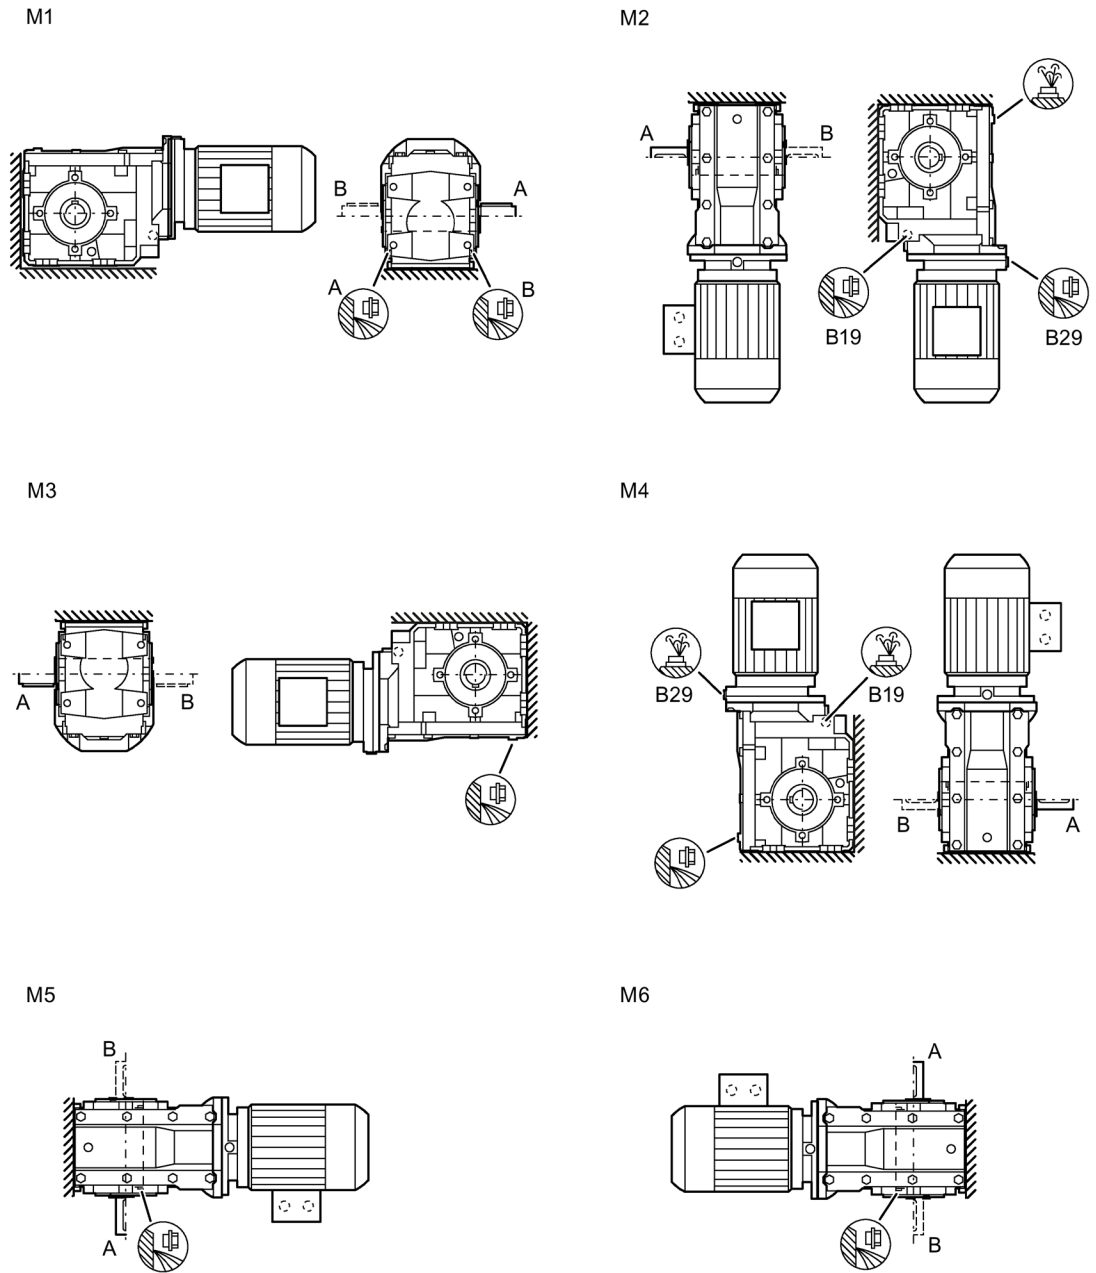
Einbaulagen für Kegelradgetriebe B. Fußausführung Baugrößen 19 - 29
